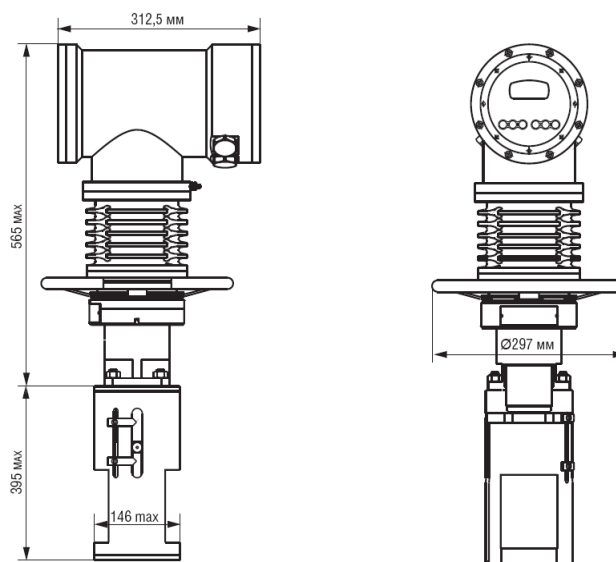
Внешний вид привода V-01-L-4,5-18000
